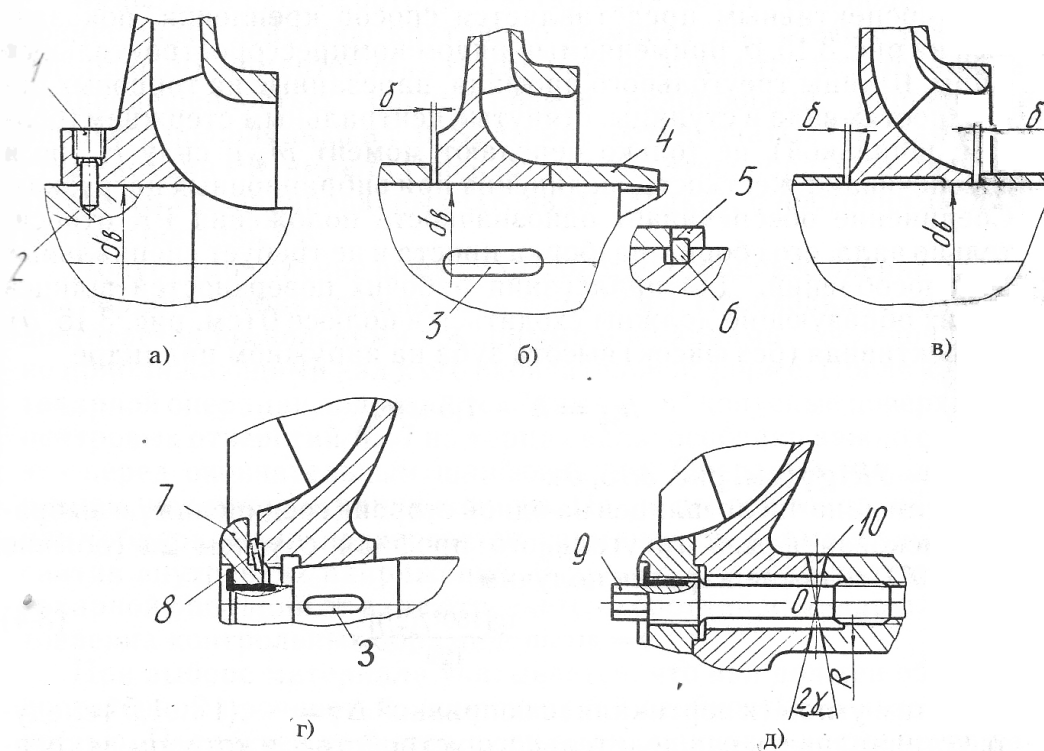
Узел крепления рабочего колеса: 1 – винт; 2 – штифт; 3 – шпонка; 4 – фиксирующая втулка; 5 – замковое кольцо; 6 – полукольца; 7 – гайка; 8 – пружинная шайба; 9 – стяжная шпилька; 10 – торцовое шлицевое соединение;  $d_s$  – диаметр вала.
